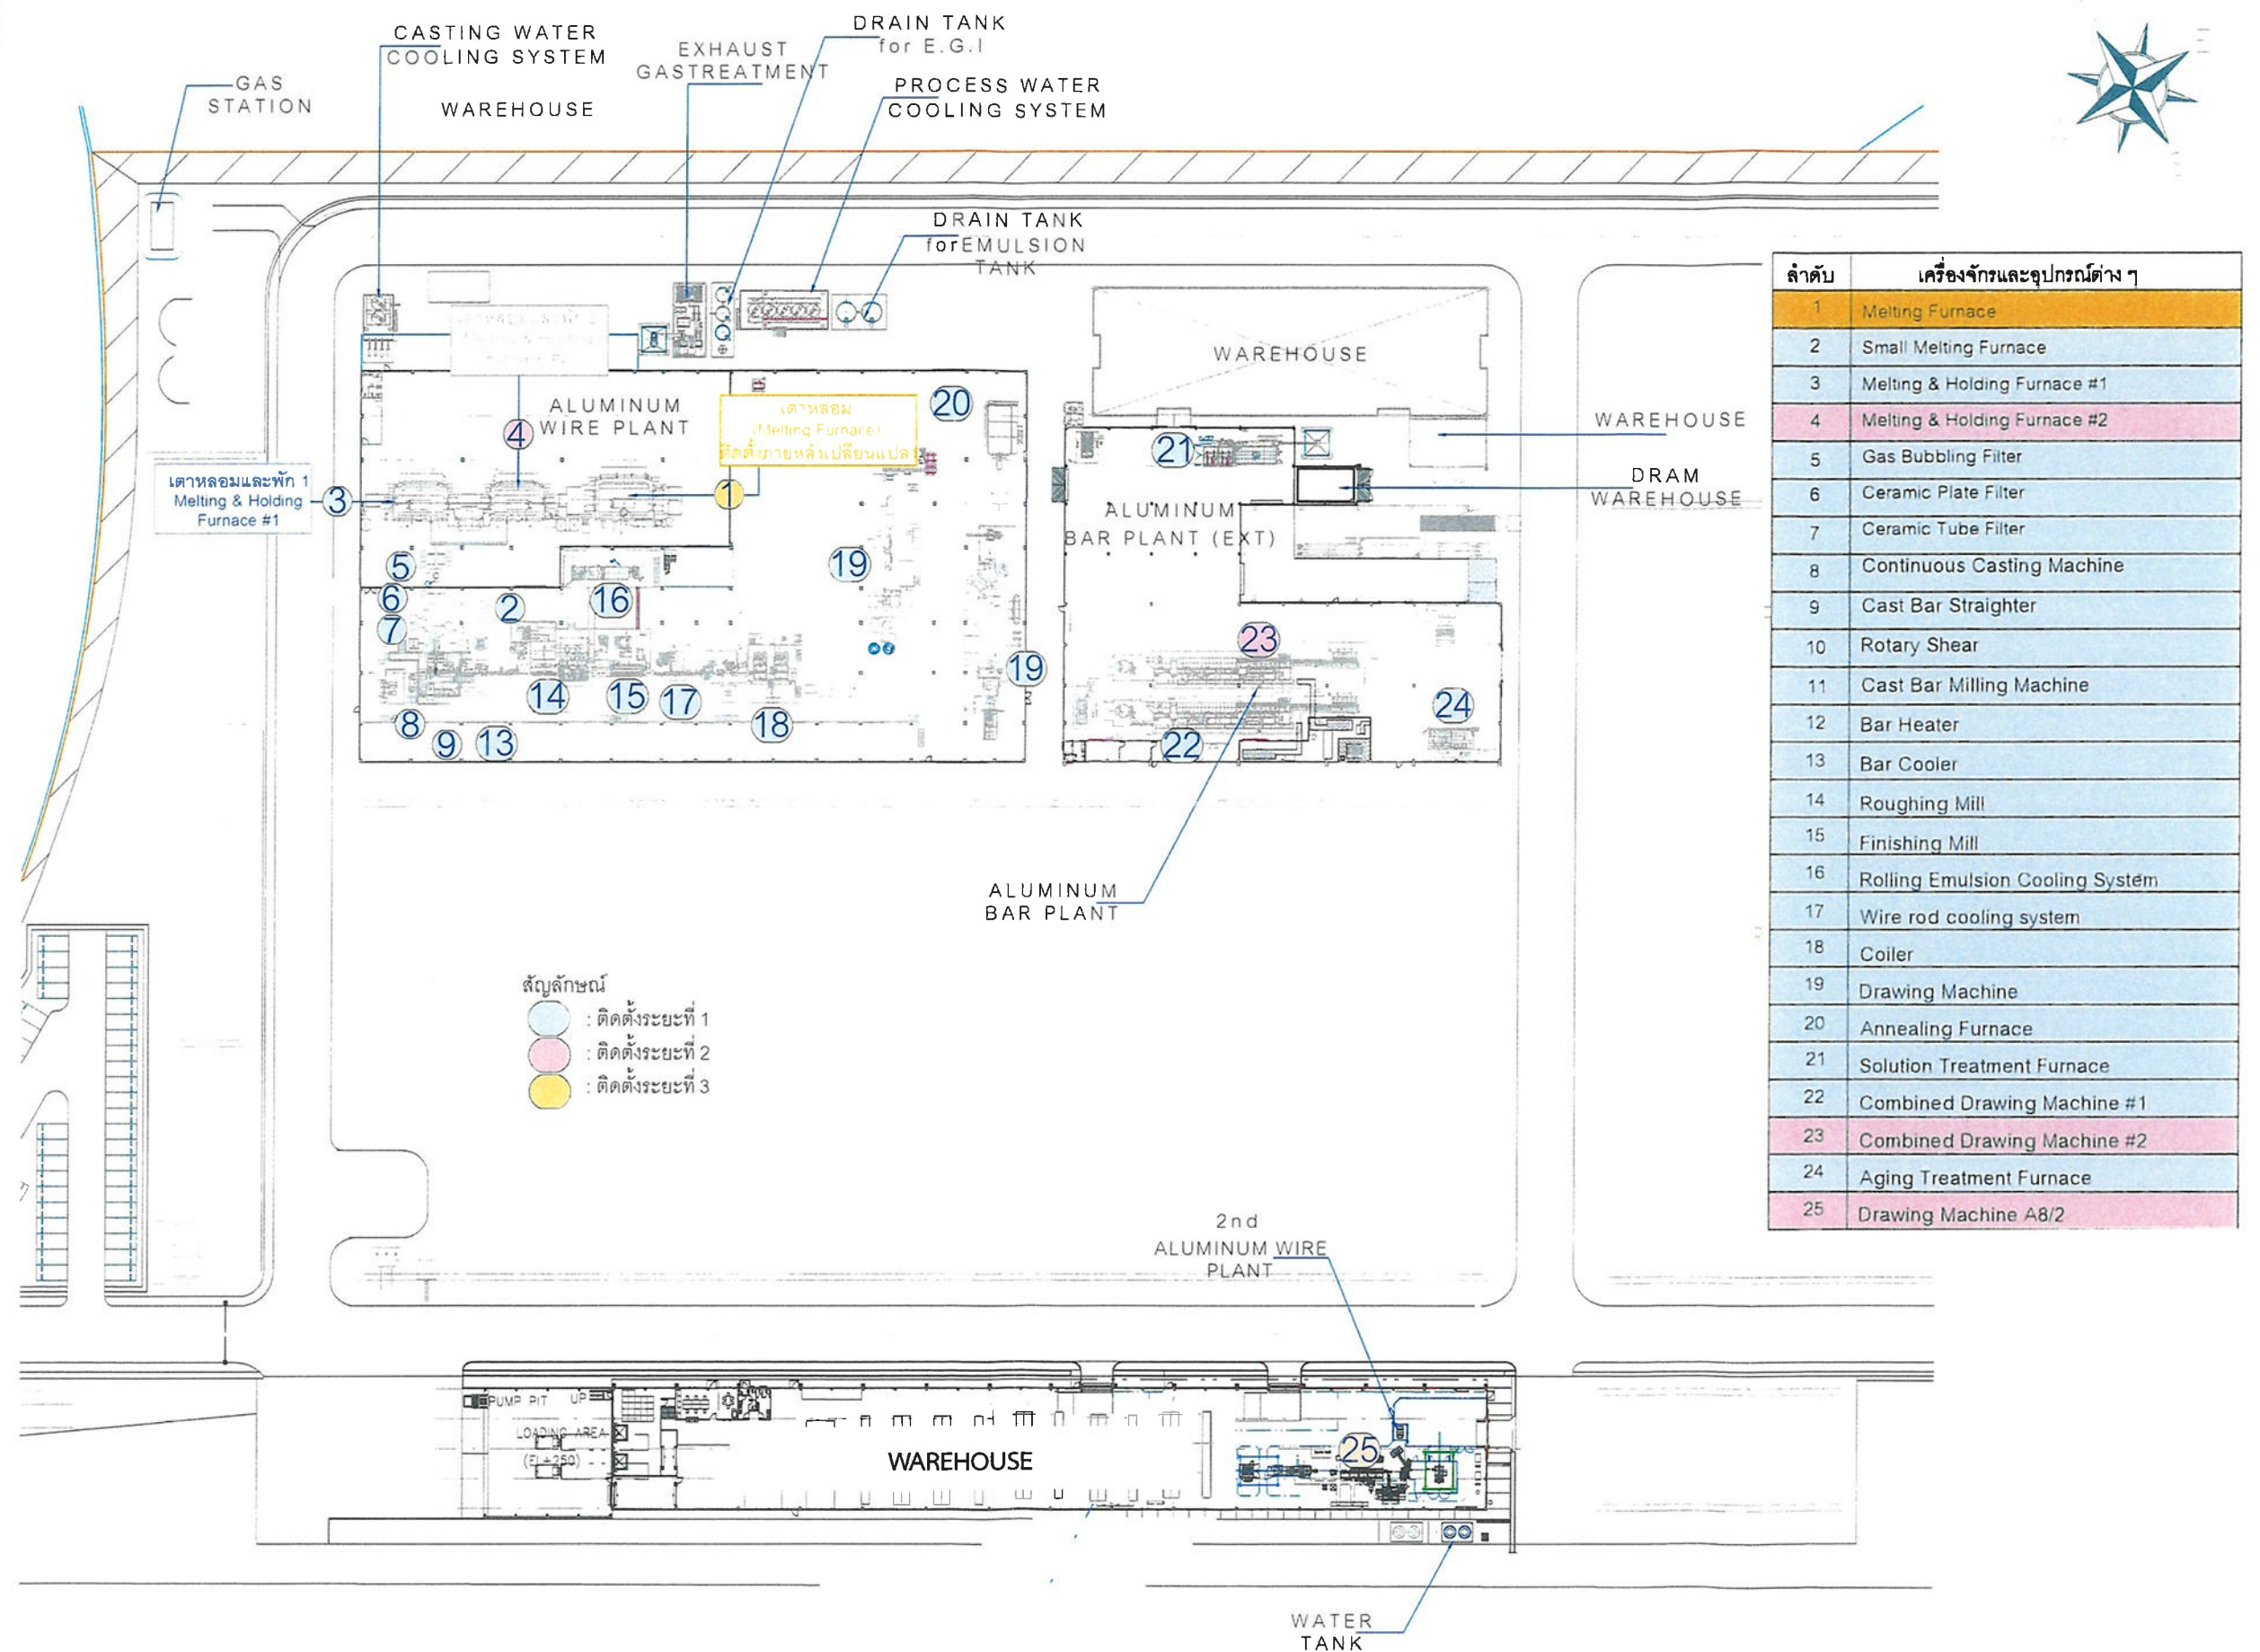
รูปแบบการเดินเครื่องสูงสุดของโครงการ (โครงการระยะที่ 3)
